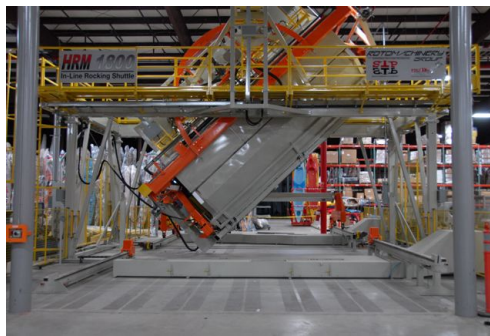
Máquina Rock an Roll - fonte: <https://rotomachinery.com>
